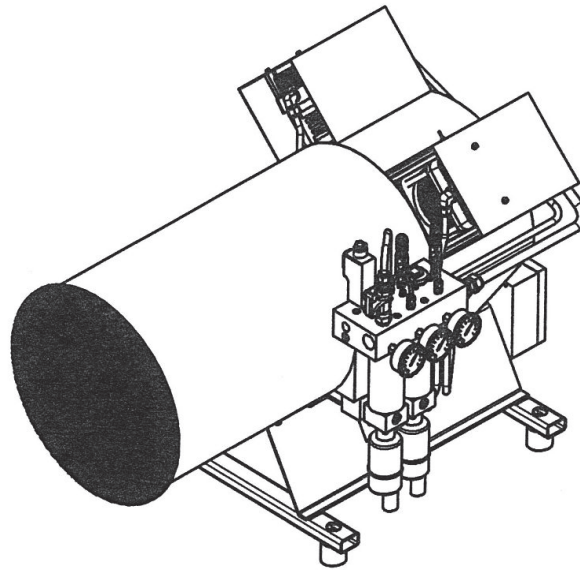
3D-Skizze des eingesetzten HAUG-Kompressors [103]
